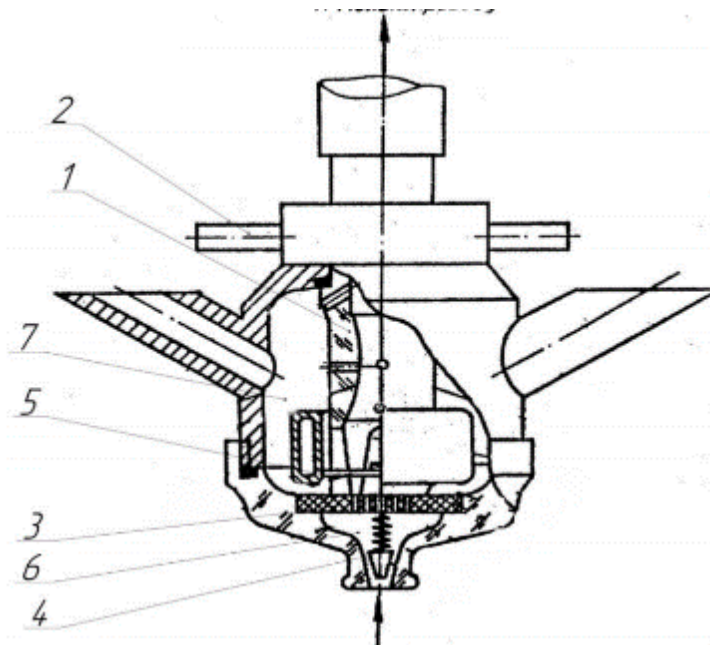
Схема колектора доїльного апарата: 1 - молочний патрубок; 2 - розподільник вакууму; 3 - сіточка; 4 - підпружинений повітряний клапан; 5 – поплавок; 6 - повітряна камера; 7 – молокозбірна камера.
